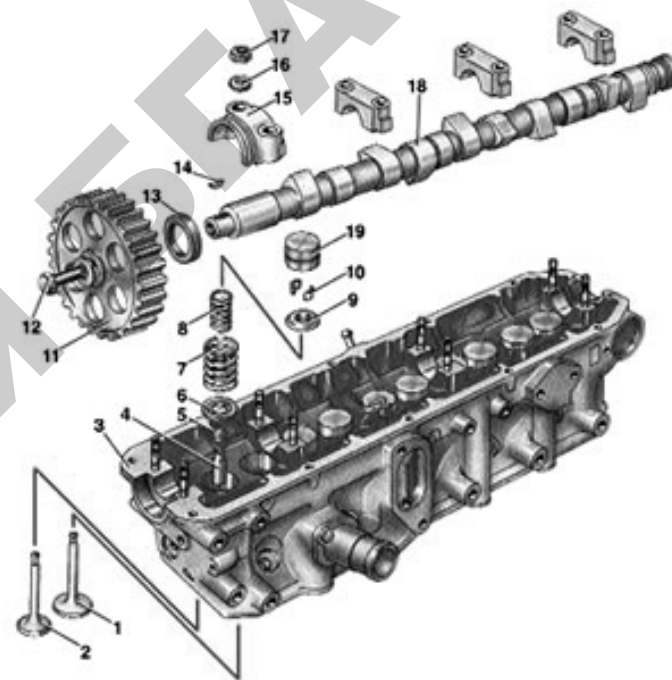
Головка блока цилиндров, распределительный вал и клапаны:
